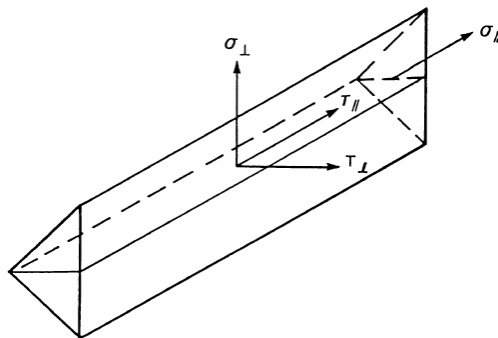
Tensões no plano que define um cordão de soldadura.
